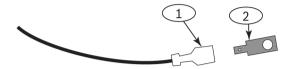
Adaptador de terminales para la conexión a la batería D1218
